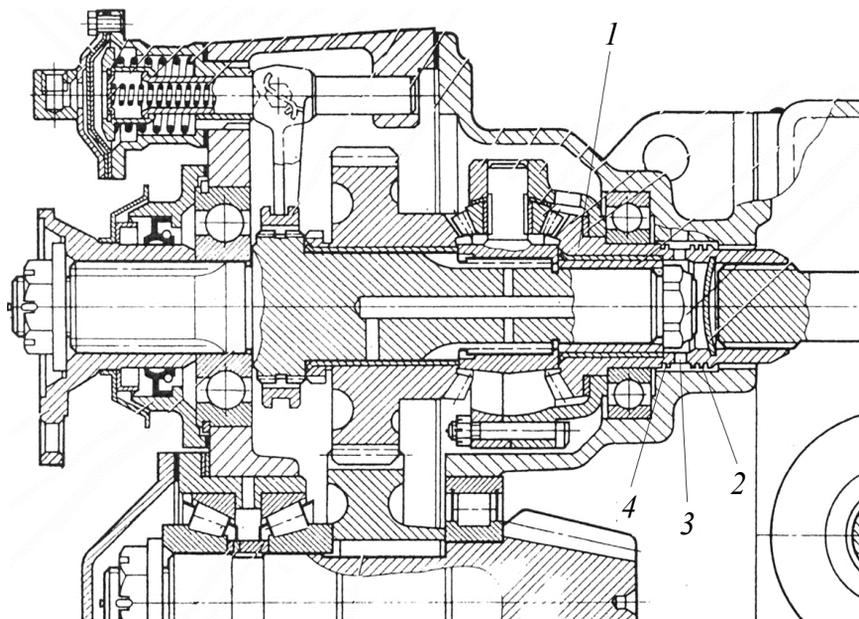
Схема подачи масла к центральному каналу ведущего вала проходного ведущего моста автомобиля ЗИЛ-133ГЯ
